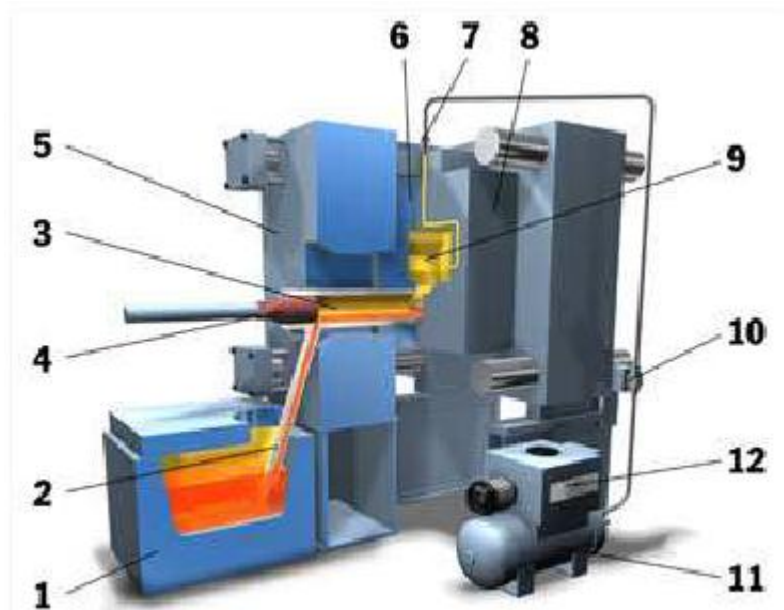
1-Forno; 2-Linha de sucção; 3-Câmara de injeção; 4-Pistão; 5-Parte fixa; 6-Parte fixa do molde; 7-Válvula de vácuo; 8-Parte móvel do molde; 9-Cavidade; 10-Válvula; 11-Bomba de vácuo; 12-Tanque de vácuo. [59]
